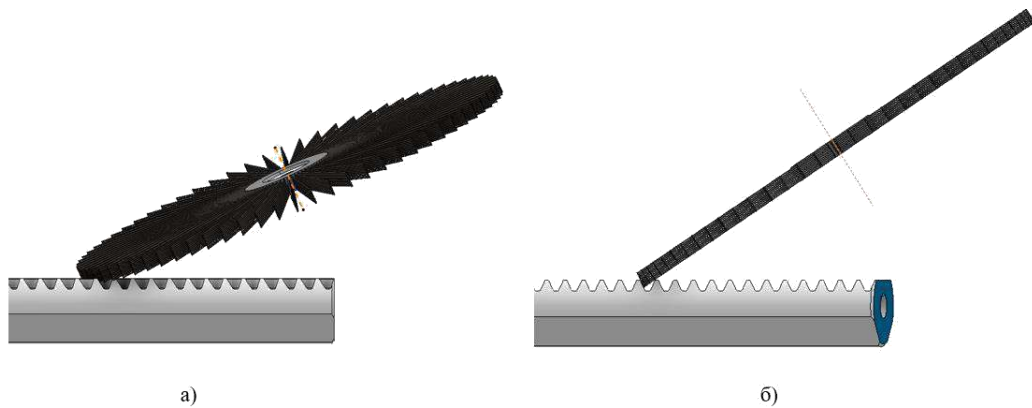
Обробка рульової рейки гнучким інструментом: а – вид збоку; б – вид нормаллю до периферії інструменту
